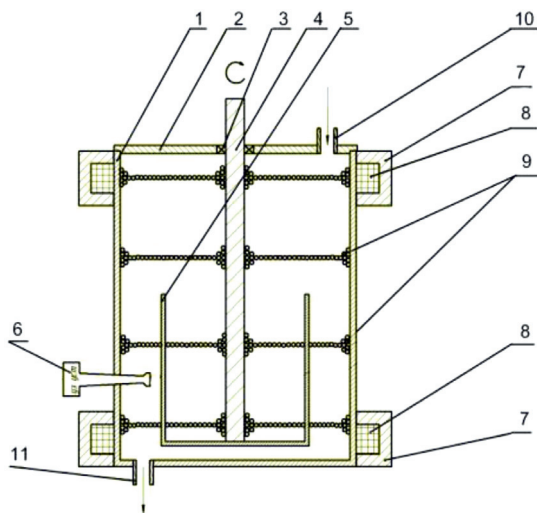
Конструктивная схема смесителя ЭМС-2 (Патент России на полезную модель № 86493): 1 – цилиндрическая камера; 2 – крышка; 3 – подшипник; 4 – ротор; 5 – лопасти; 6 – источник УЗ; 7 – ферромагнитное кольцо; 8 – ОУ; 9 – ферромагнитные цилиндры; 10, 11 – патрубки для входа и выхода смеси
